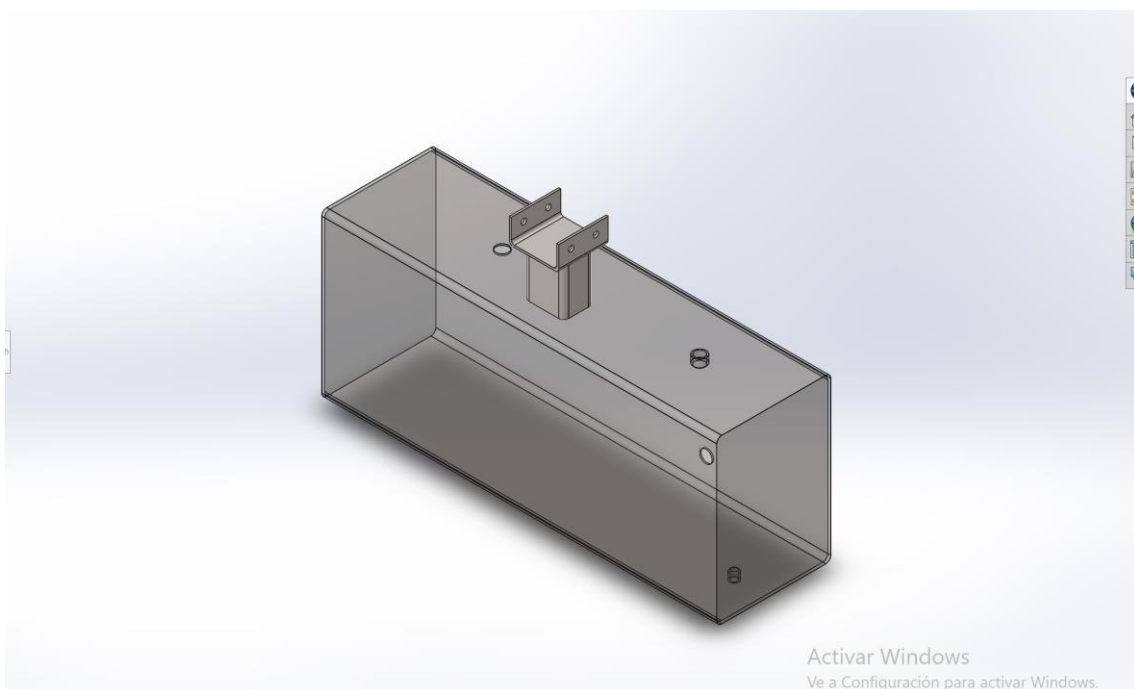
Diseño y montaje de perfiles rectangulares y U.
